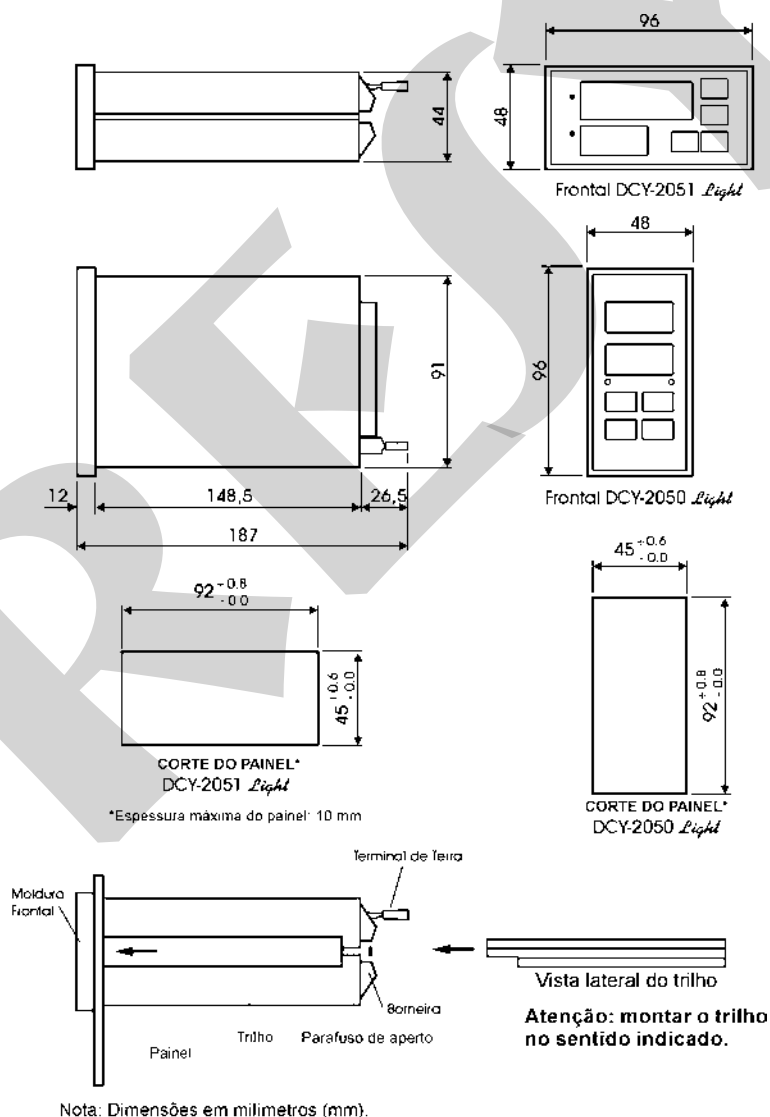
Desenho dimensional, corte e vista lateral da montagem no painel dos controladores DCY-2050/2051 *Light
